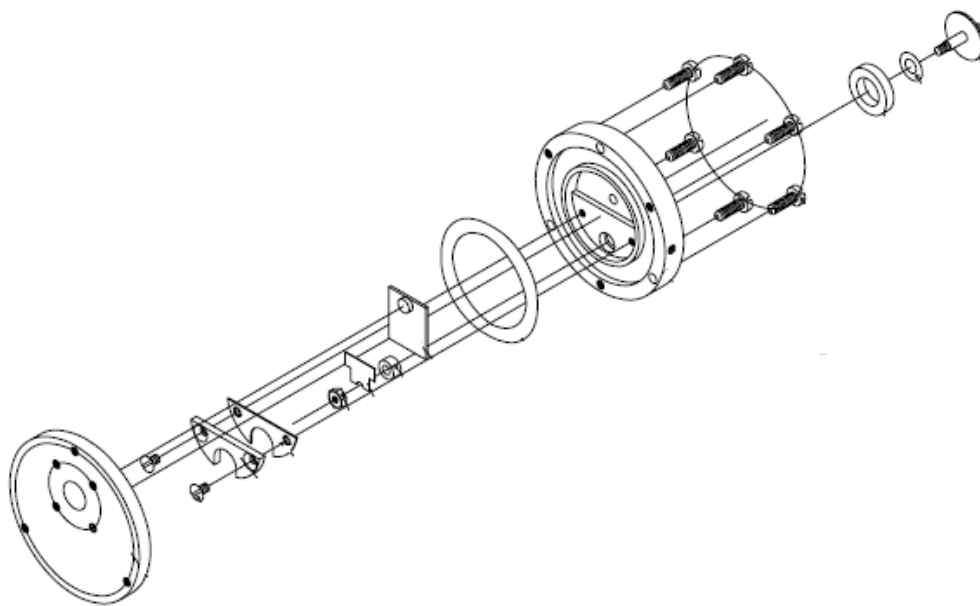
Piezas y esquema de montaje de la válvula piezoeléctrica según el diseño original del Prof. Dieter Gerlich, de la Universidad de Chemnitz, Alemania. Tomado de la página web http://www.tu-chemnitz.de/physik/ION/Technology/Piezo_Valve/index.html.
